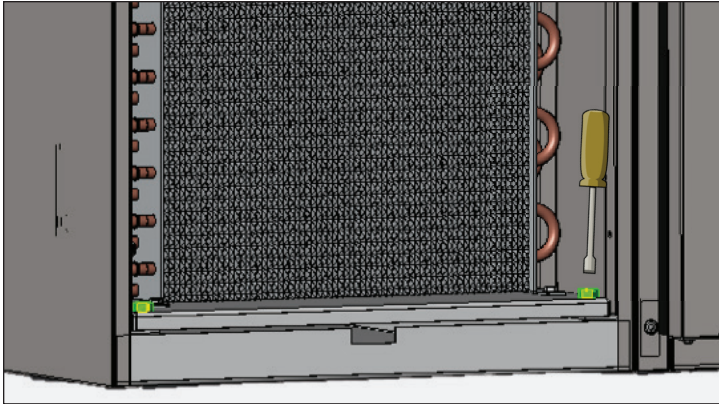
Die Schrauben aus der unteren Platte des Verflüssigers entfernen
